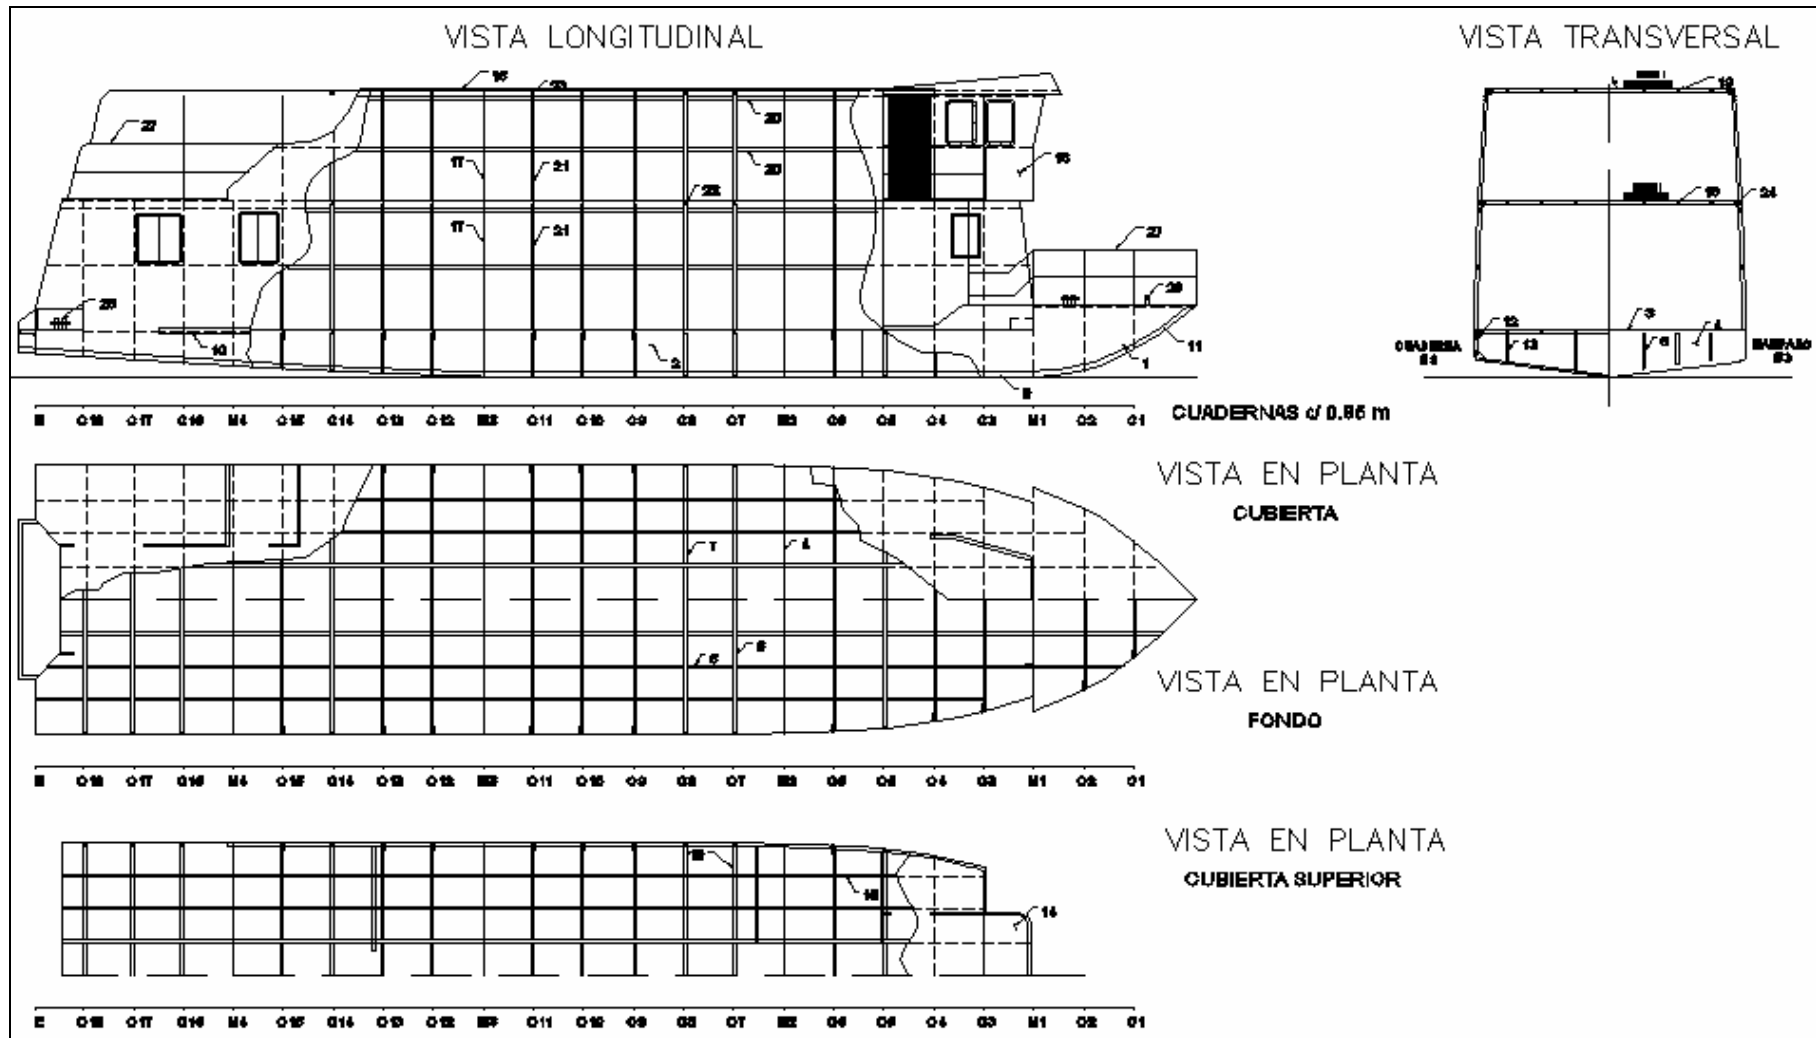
Plano de estructurales de la lancha hospital Samarina, [13]
